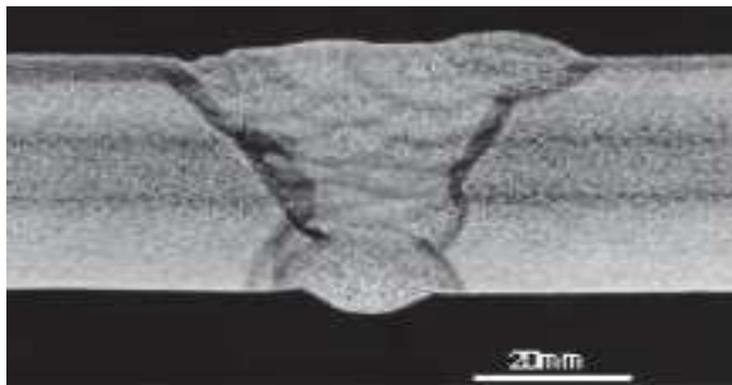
Manque de fusion dans le flanc de la soudure.
